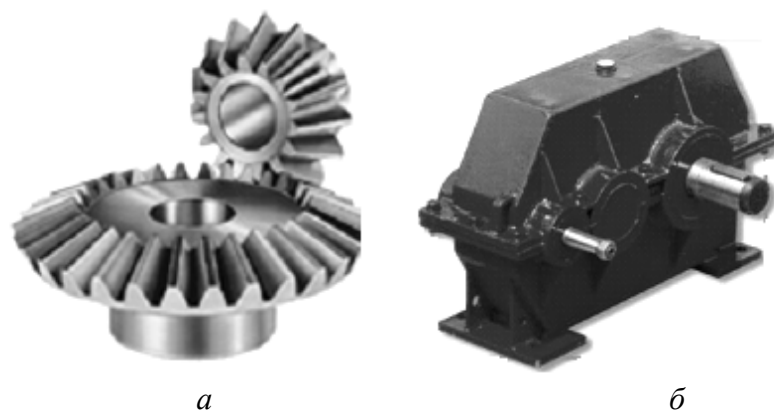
Конструктивное исполнение зубчатых передач:
